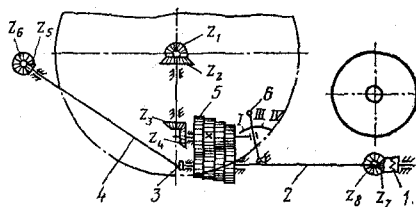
Схема механизма передачи движения суппорту и каретке перевивочного механизма
